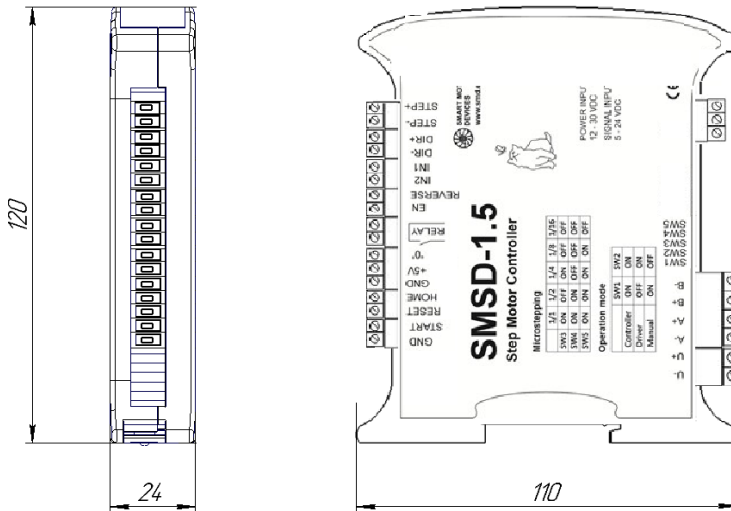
Габаритные размеры блока управления SMSD-1.5 RS-485
